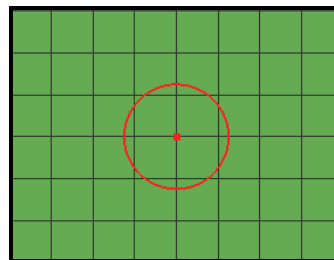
Ponto de solda tipo 1, elemento do tipo *spot weld* concêntrico
